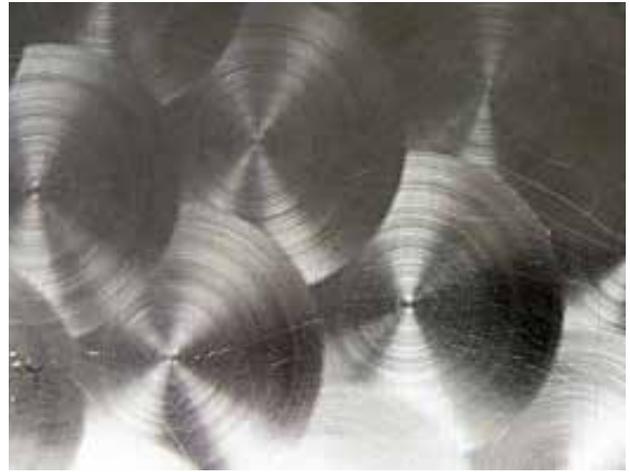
Отфрезерованная поверхность нержавеющей стали
